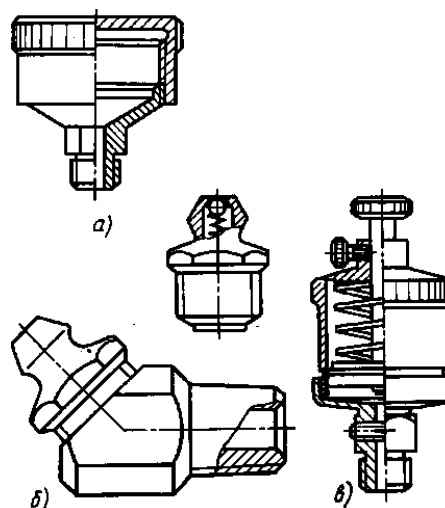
Масленки для подачи пластичного смазочного материала:
